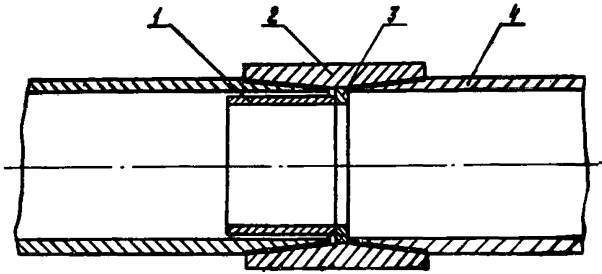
Установка образца внутри насосно-компрессорных труб:
